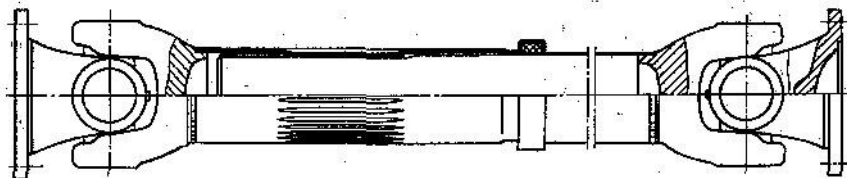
Карданный вал облегченной конструкции, изготавливаемый из стали фирмой «Кляйн»
